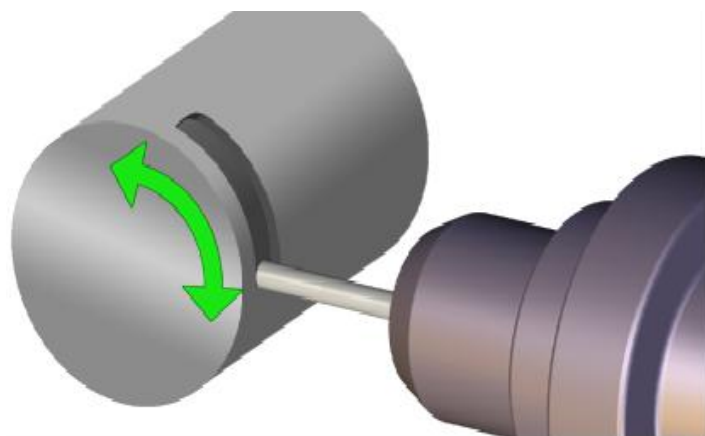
Praktická ukázka - radiální frézování s natáčením osy C v ose obrobku [19]
